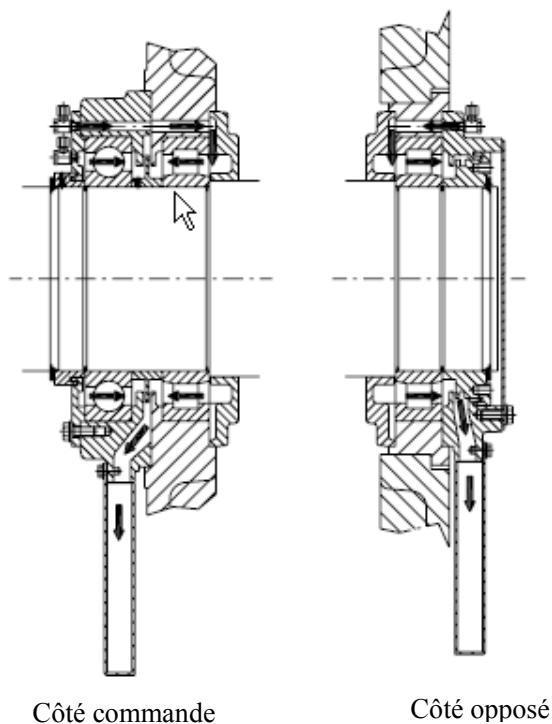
Exemple de canal de lubrification à travers le palier d'une machine horizontale.
